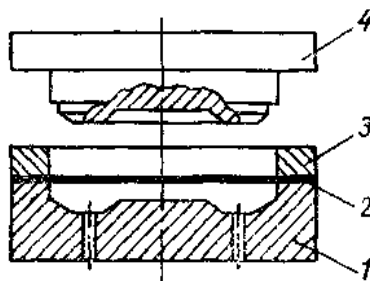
Схема штампування листових термопластів: 1 – матриця; 2 – вихідна заготовка; 3 – притискне кільце; 4 – пуансон
